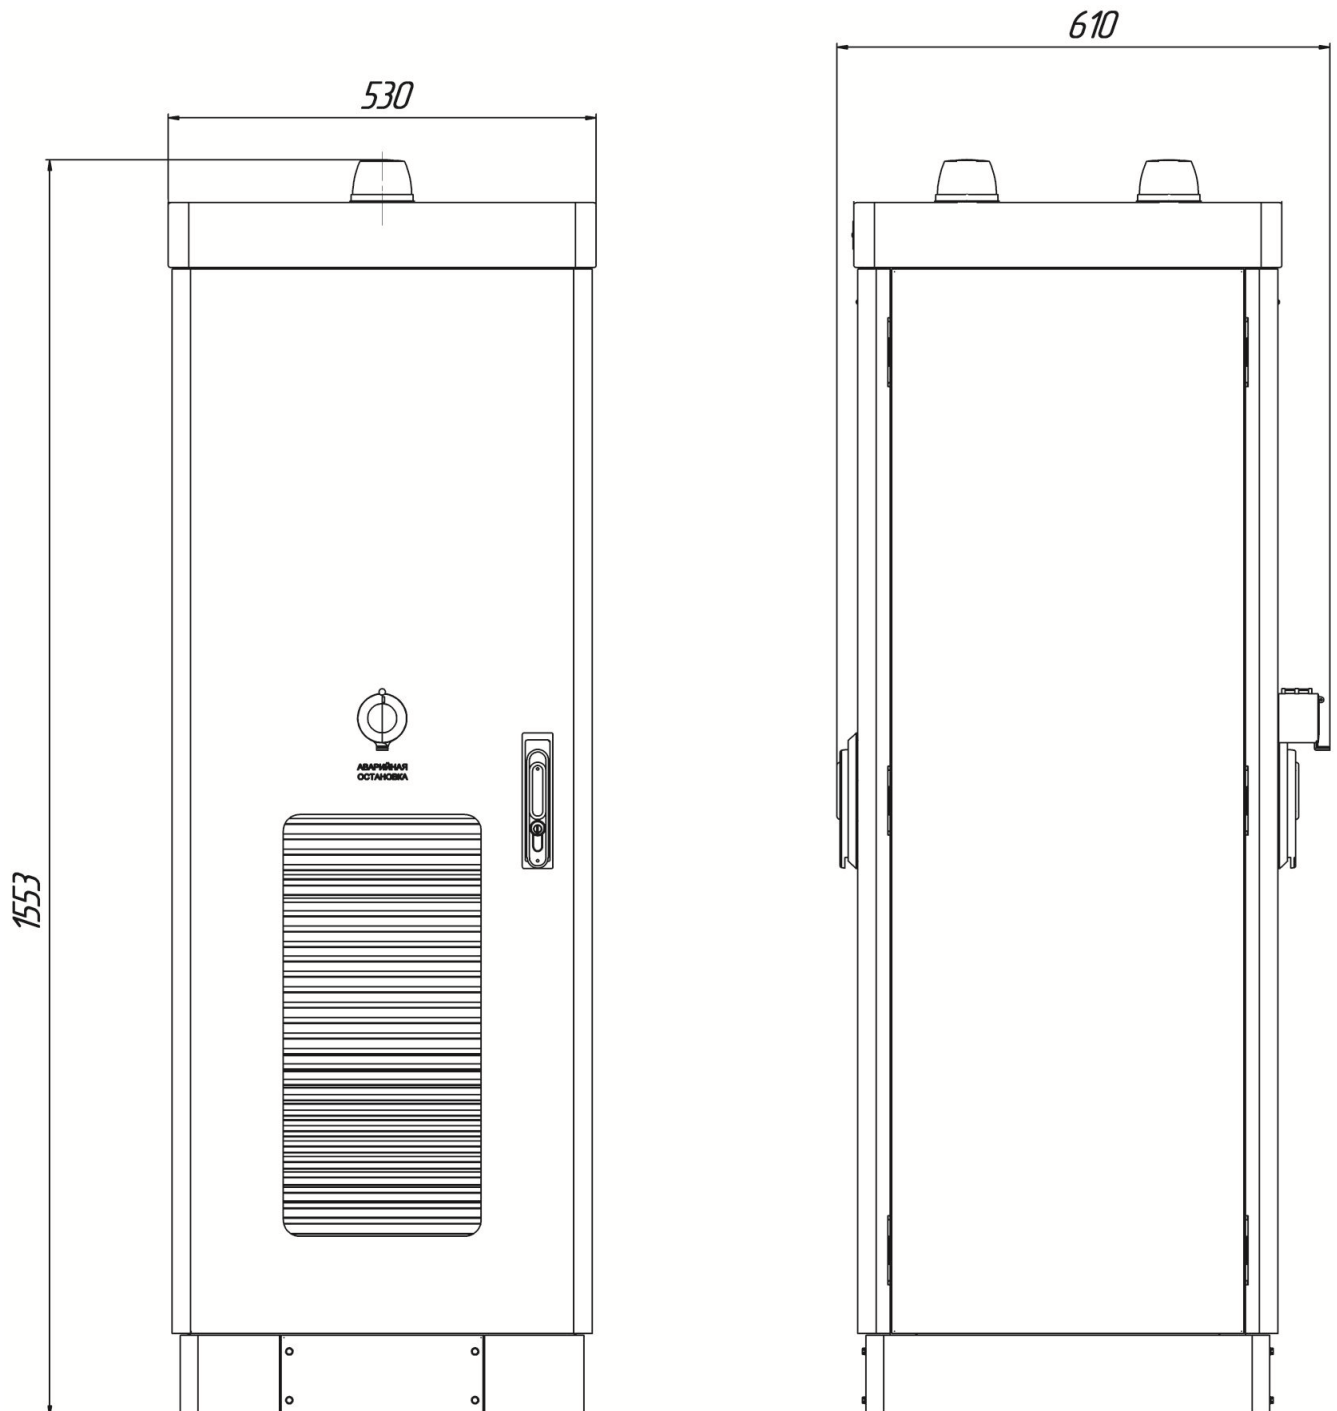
Габаритный чертеж модуля силового МС-120
